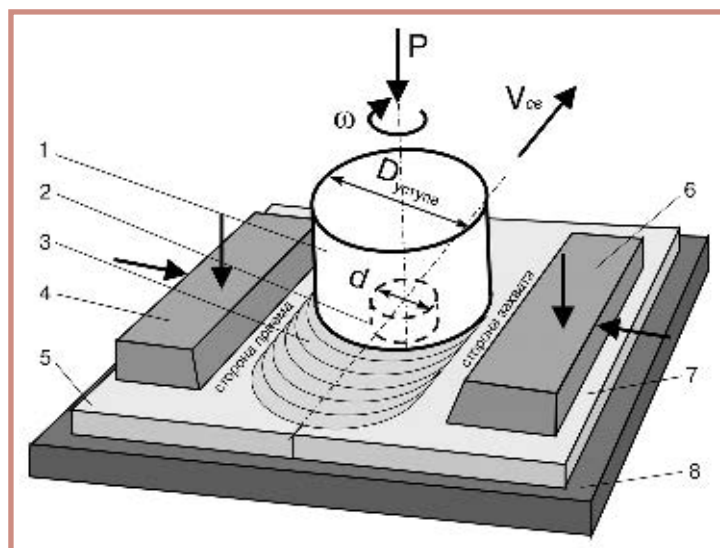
Схема выполнения СТП: 1 — сварочный инструмент; 2 — наконечник сварочного инструмента; 3 — сварной шов; 4, 6 — прижимные планки; 5, 7 — свариваемые заготовки; 8 — технологическая подкладка (ω — скорость вращения сварочного инструмента; $V_{св}$ — скорость сварки; $D_{уст}$ — диаметр опорной поверхности уступа сварочного инструмента; P — осевое давление сварочного инструмента на свариваемые заготовки)
